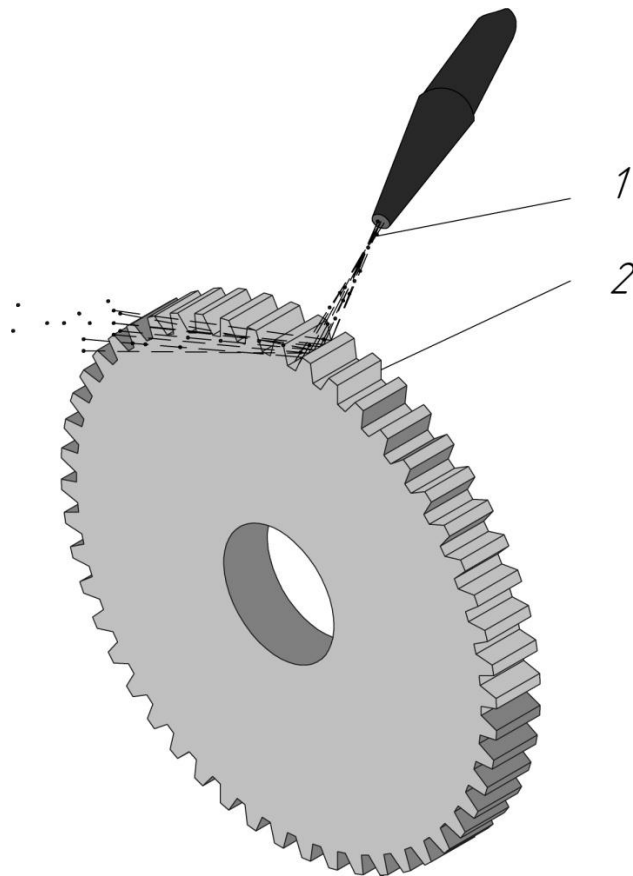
Дробоструменева обробка зубчастих коліс
